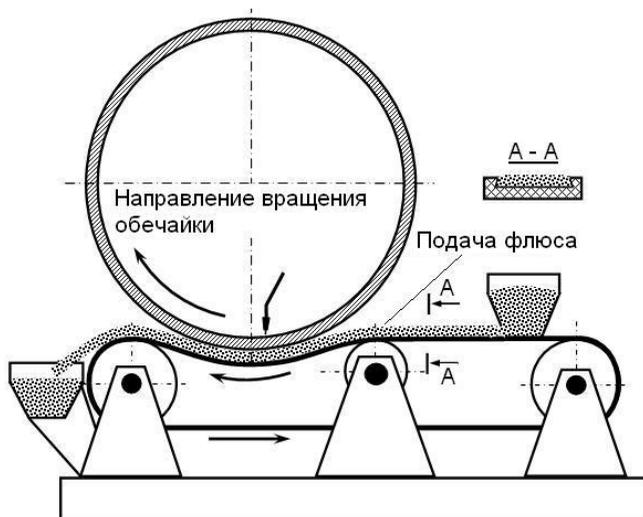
Флюсоремненная подушка для сварки кольцевых швов.
